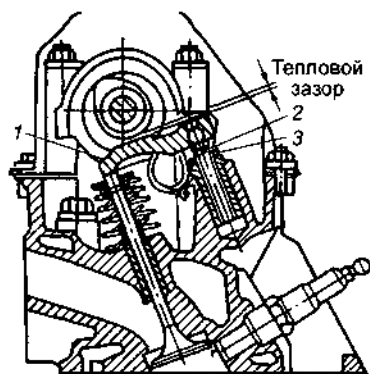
Регулировка тепловых зазоров ГРМ двигателя автомобиля марки «ВАЗ» классической компоновки: 1 — коромысло; 2 — регулировочный винт; 3 — контргайка
